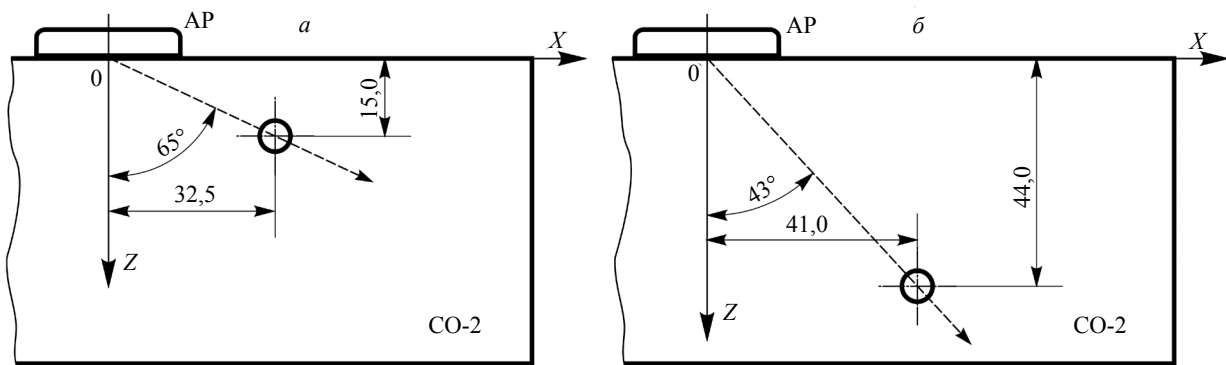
Схемы взаимного расположения антенной решетки и бокового цилиндрического отверстия.
